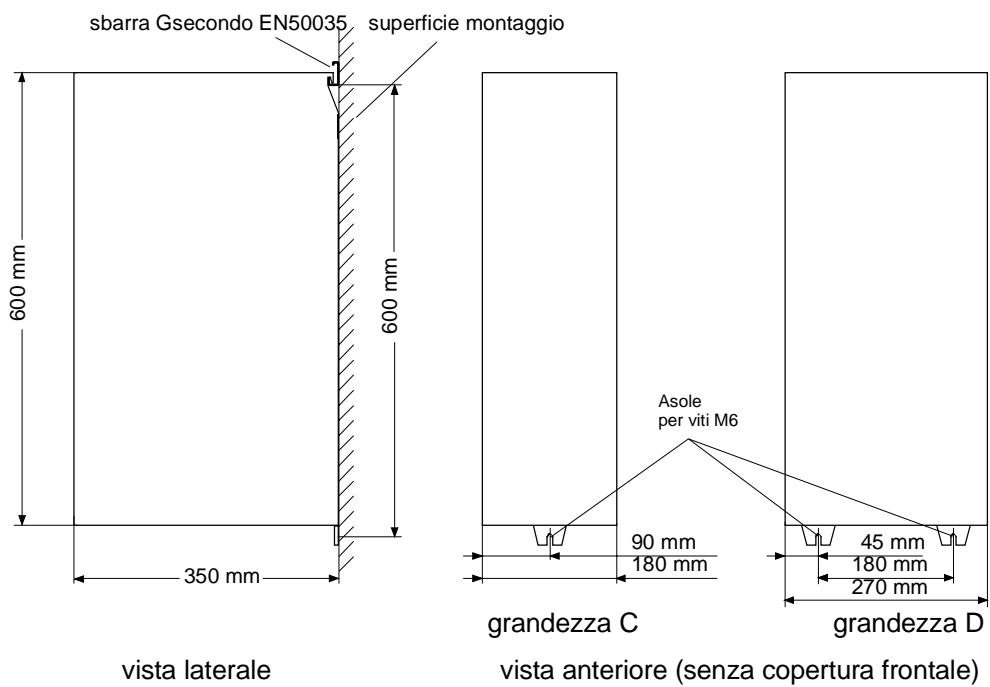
Disegni d'ingombro per montaggio grandezze C, D
